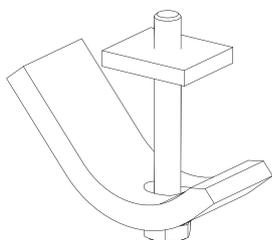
Griffes de serrage, épaisseur de serrage 18-36 mm (acier galvanisé ou V4A)
